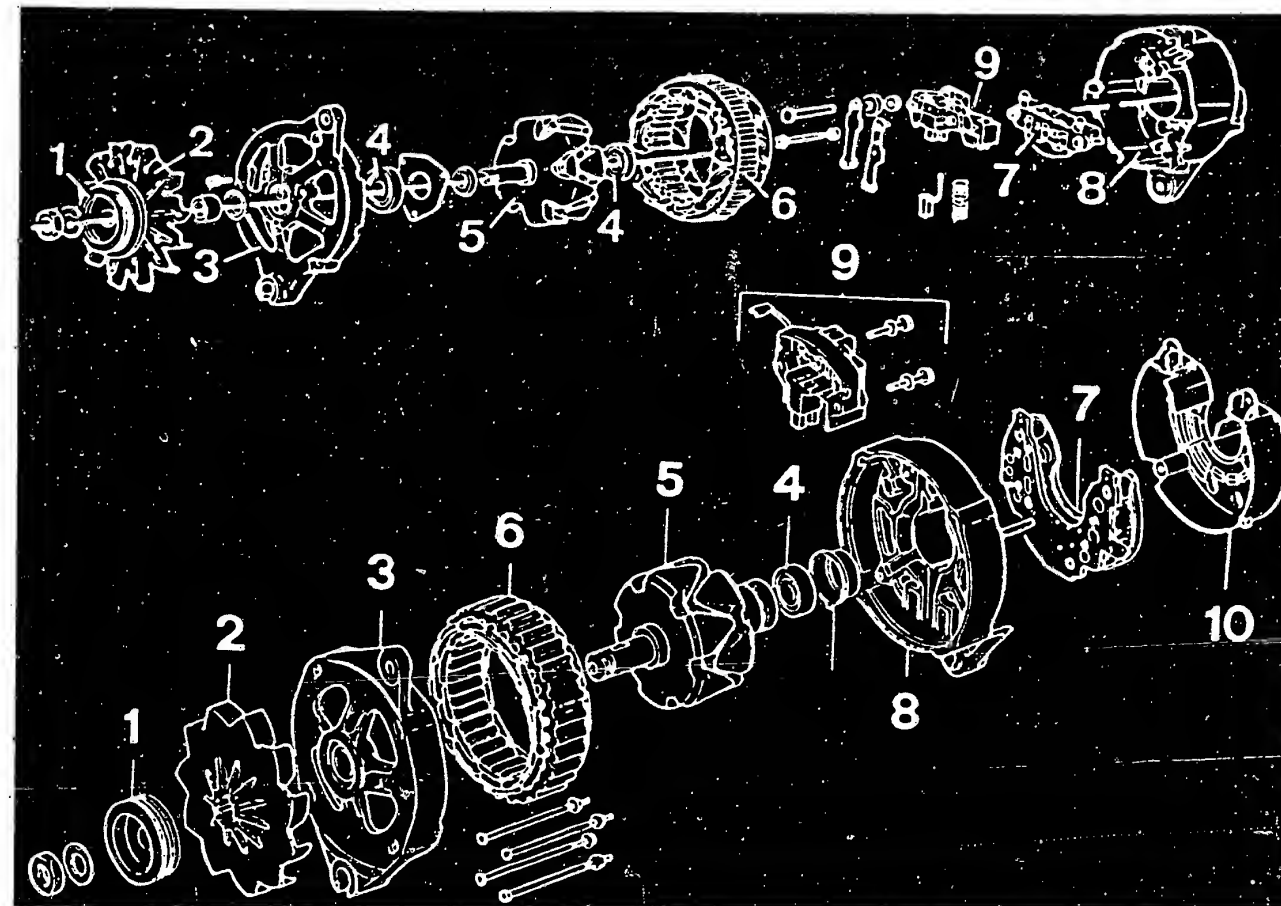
Die Alternatoren von Mitsubishi (oben) und Paris-Rhône. 1 Keilriemenrad – 2 Lüfterrad – 3 Vorderer Gehäuseteil – 4 Lager – 5 Rotor – 6 Stator – 7 Diodenplatte – 8 Hinterer Gehäuseteil – 9 Kohlebürstenträger und Regler.
